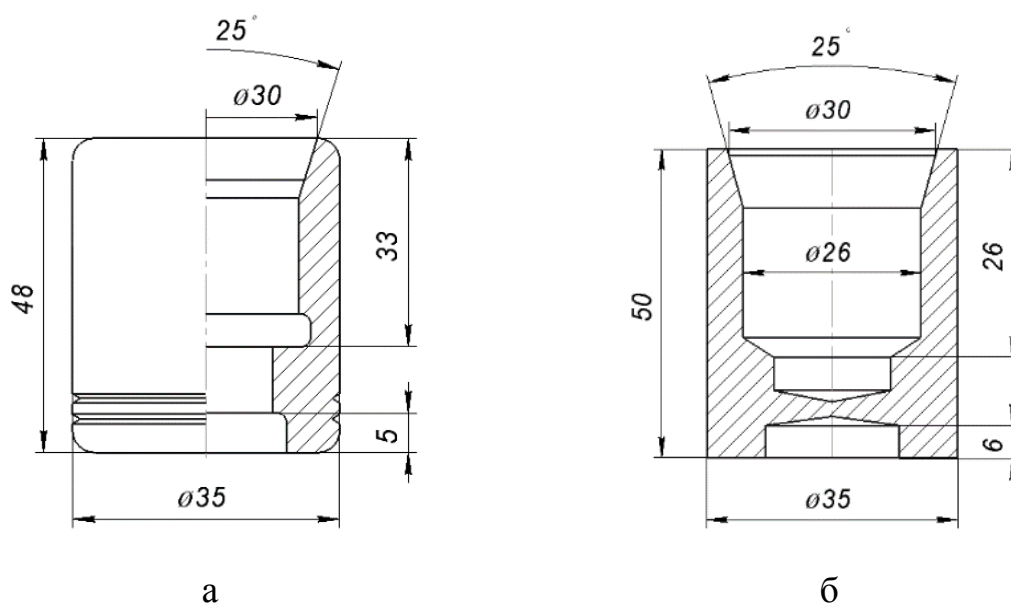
Креслення втулки для обробки різанням і видавлюванням
